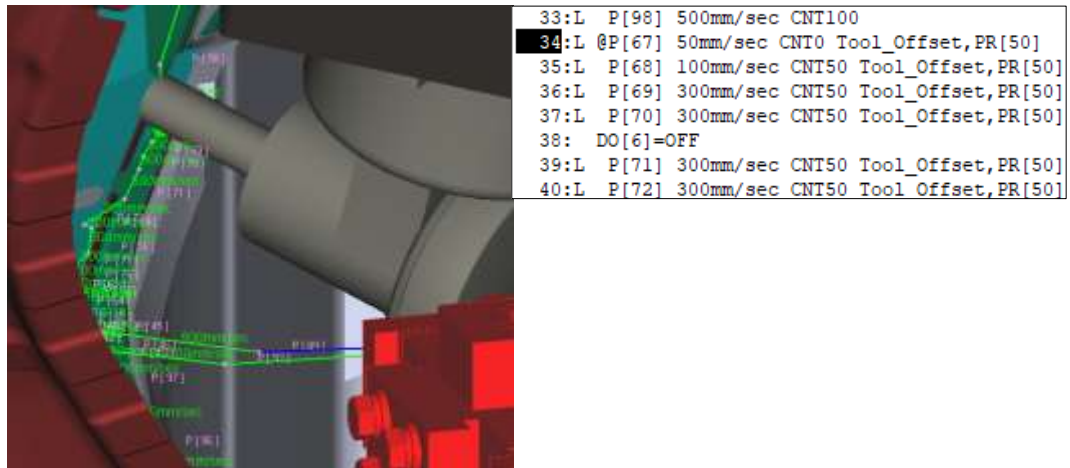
Robot B usando la roldana pequeña para el engrapado a 45°
